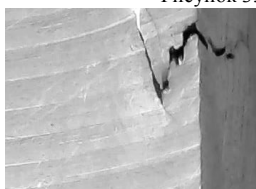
Трещины в растянутой зоне сварного соединения во время проведения испытания.
